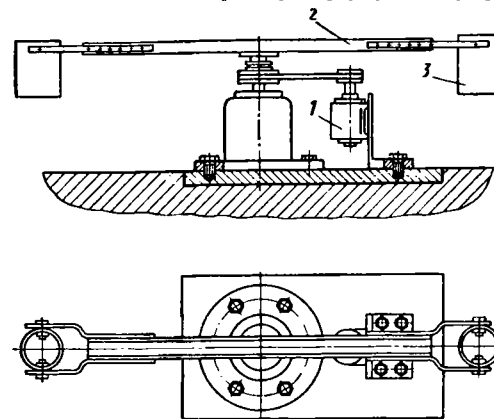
Схема установки (центрифуги) для центробежной заливки разовых форм:
